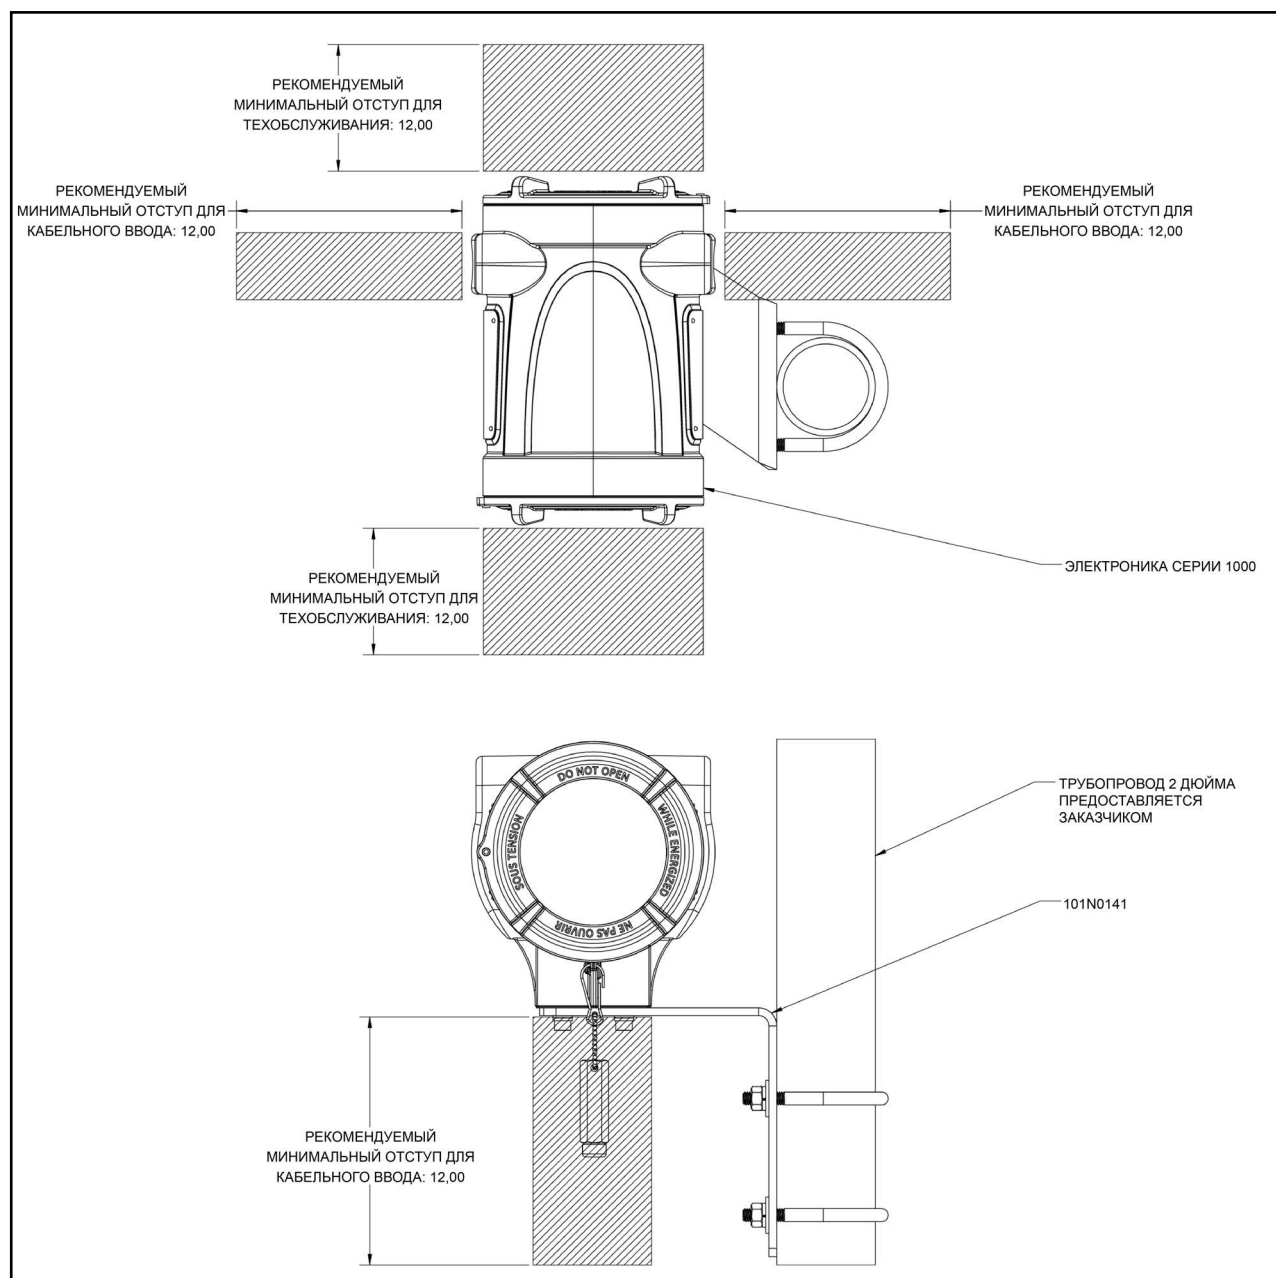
Размеры отступов для корпуса ХМТ1000 (чертеж 712-2164)
